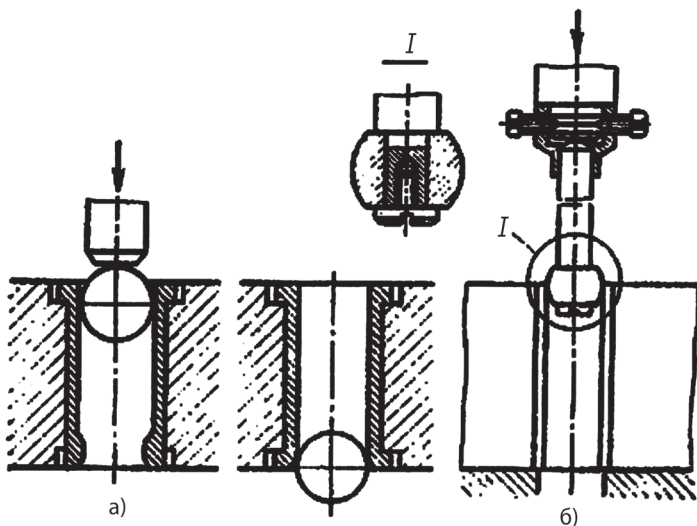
Калибровка подшипников-втулок после запрессовки:
